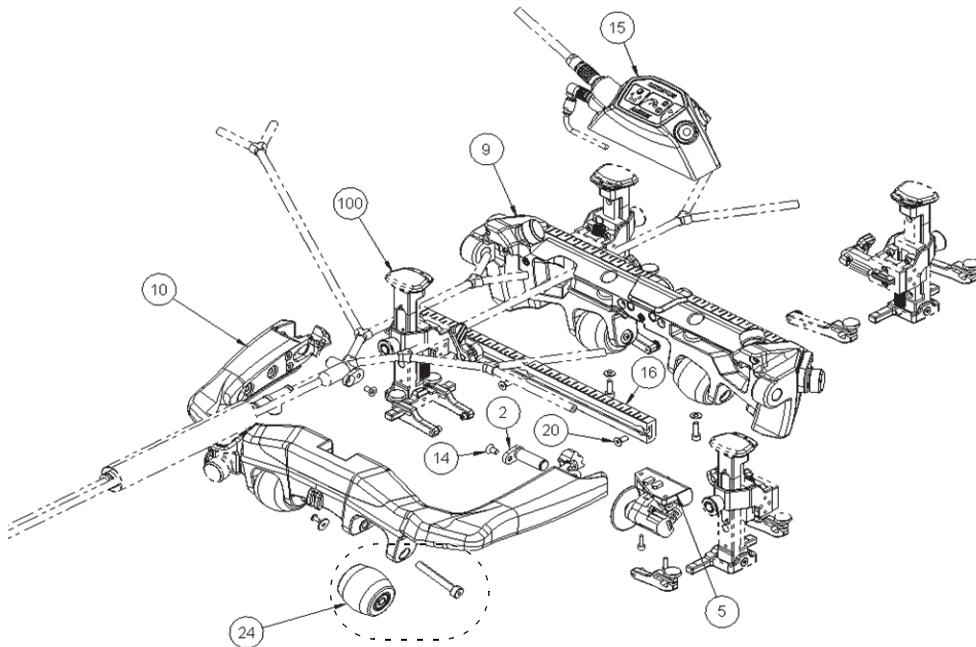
Vue éclatée — Assemblage du scanner (vue de dessus)
